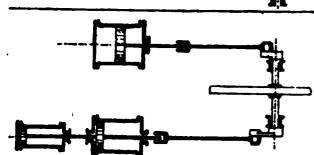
Dreifach - Expansions-Tandemmaschine. 2Kurbeln unter 900 versetzt. Für stationäre Maschinen viel angewandt.
